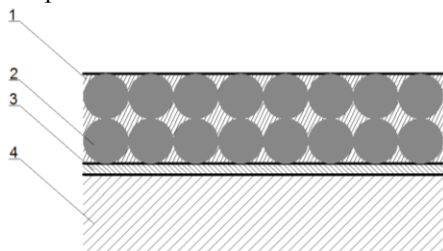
Схема металлофторопластового ленточного материала:
